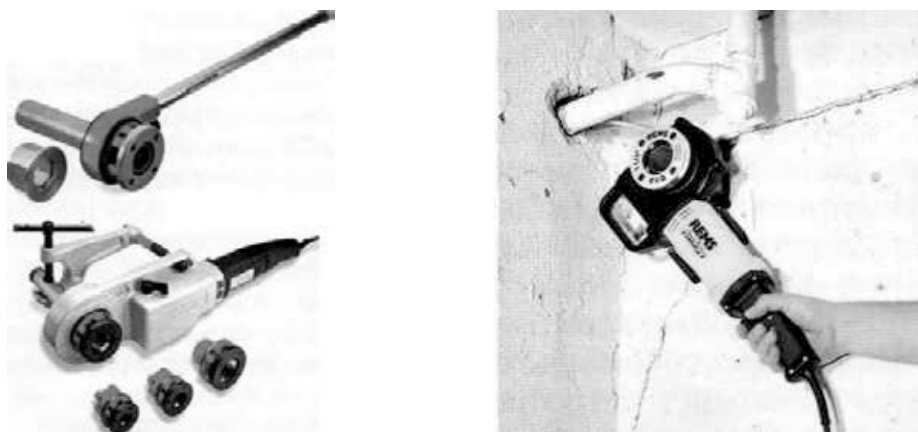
Інструмент для нарізання різьби – ручний та електричний клупп.
